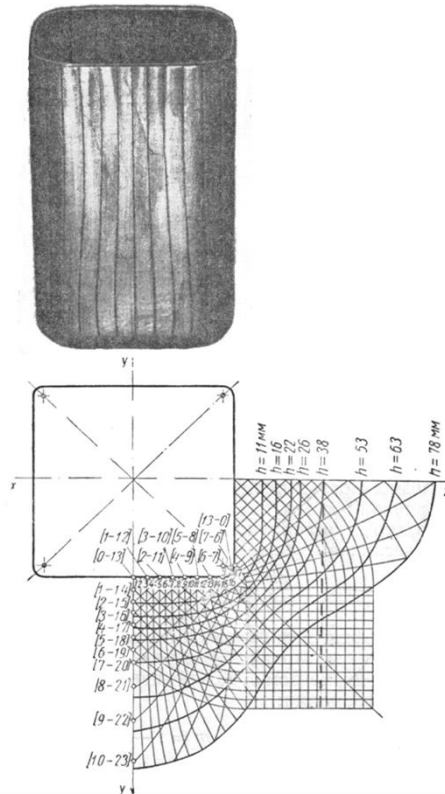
Розміри і форма оптимальних заготовок для витяжки квадратних коробок різної висоти та деталь, одержана із оптимальної заготовки ($H/B=0,95$) [9].
